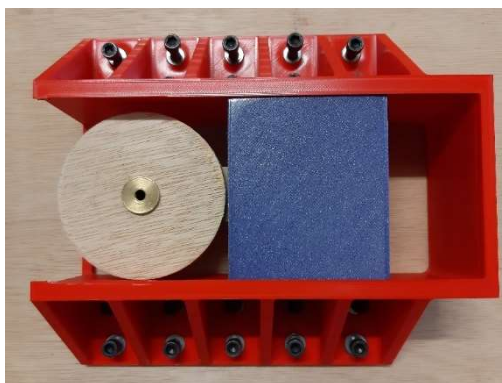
Posicionament conjunt corró-pistó a dins la Guia 3D.
